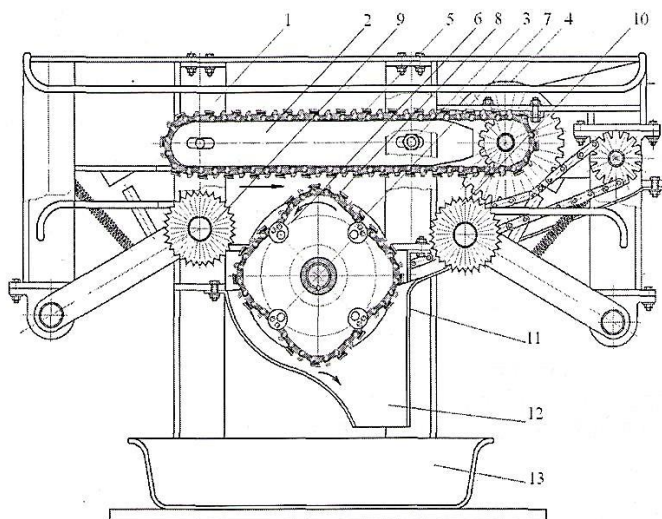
Устройство для заготовки хвойной лапки (вид сбоку)
